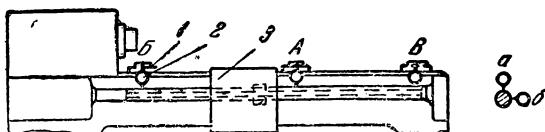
Проверка совпадения осей отверстий для инструментов с осью вращения шпинделя револьверного станка.
